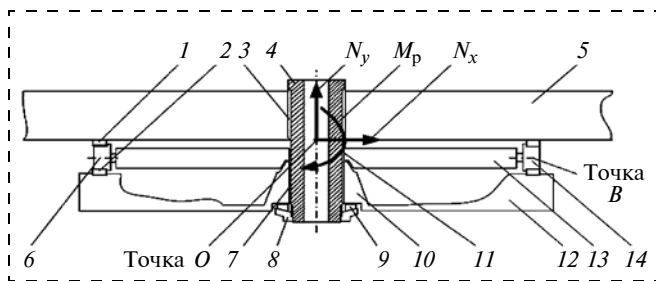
Схема общей конструкции опорно-поворотного устройства и расположения реакций связей: 1 – верхний рельс; 2 – нижний рельс; 3 – втулка (верхний и нижний пояса) поворотной платформы; 4 – центральная цапфа; 5 – поворотная платформа; 6 – роликовый круг; 7 – втулка нижней рамы; 8 – гайка центральной цапфы; 9 – сферическая шайба; 10 – отливка нижней рамы; 11 – втулка сепаратора роликового круга; 12 – нижняя рама; 13 – сепаратор роликового круга; 14 – передний ролик (точка B); N_x – горизонтальная составляющая нагрузок; N_y – вертикальная составляющая нагрузок; M_p – реактивный (изгибающий) момент
